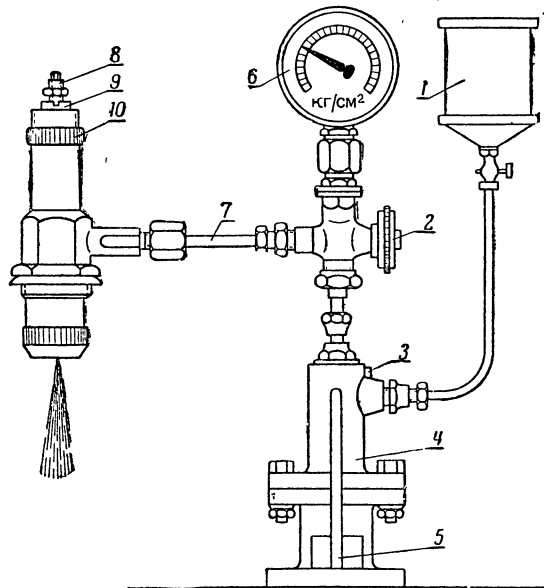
91. Схема прибора МД-25 для испытания форсунок:
